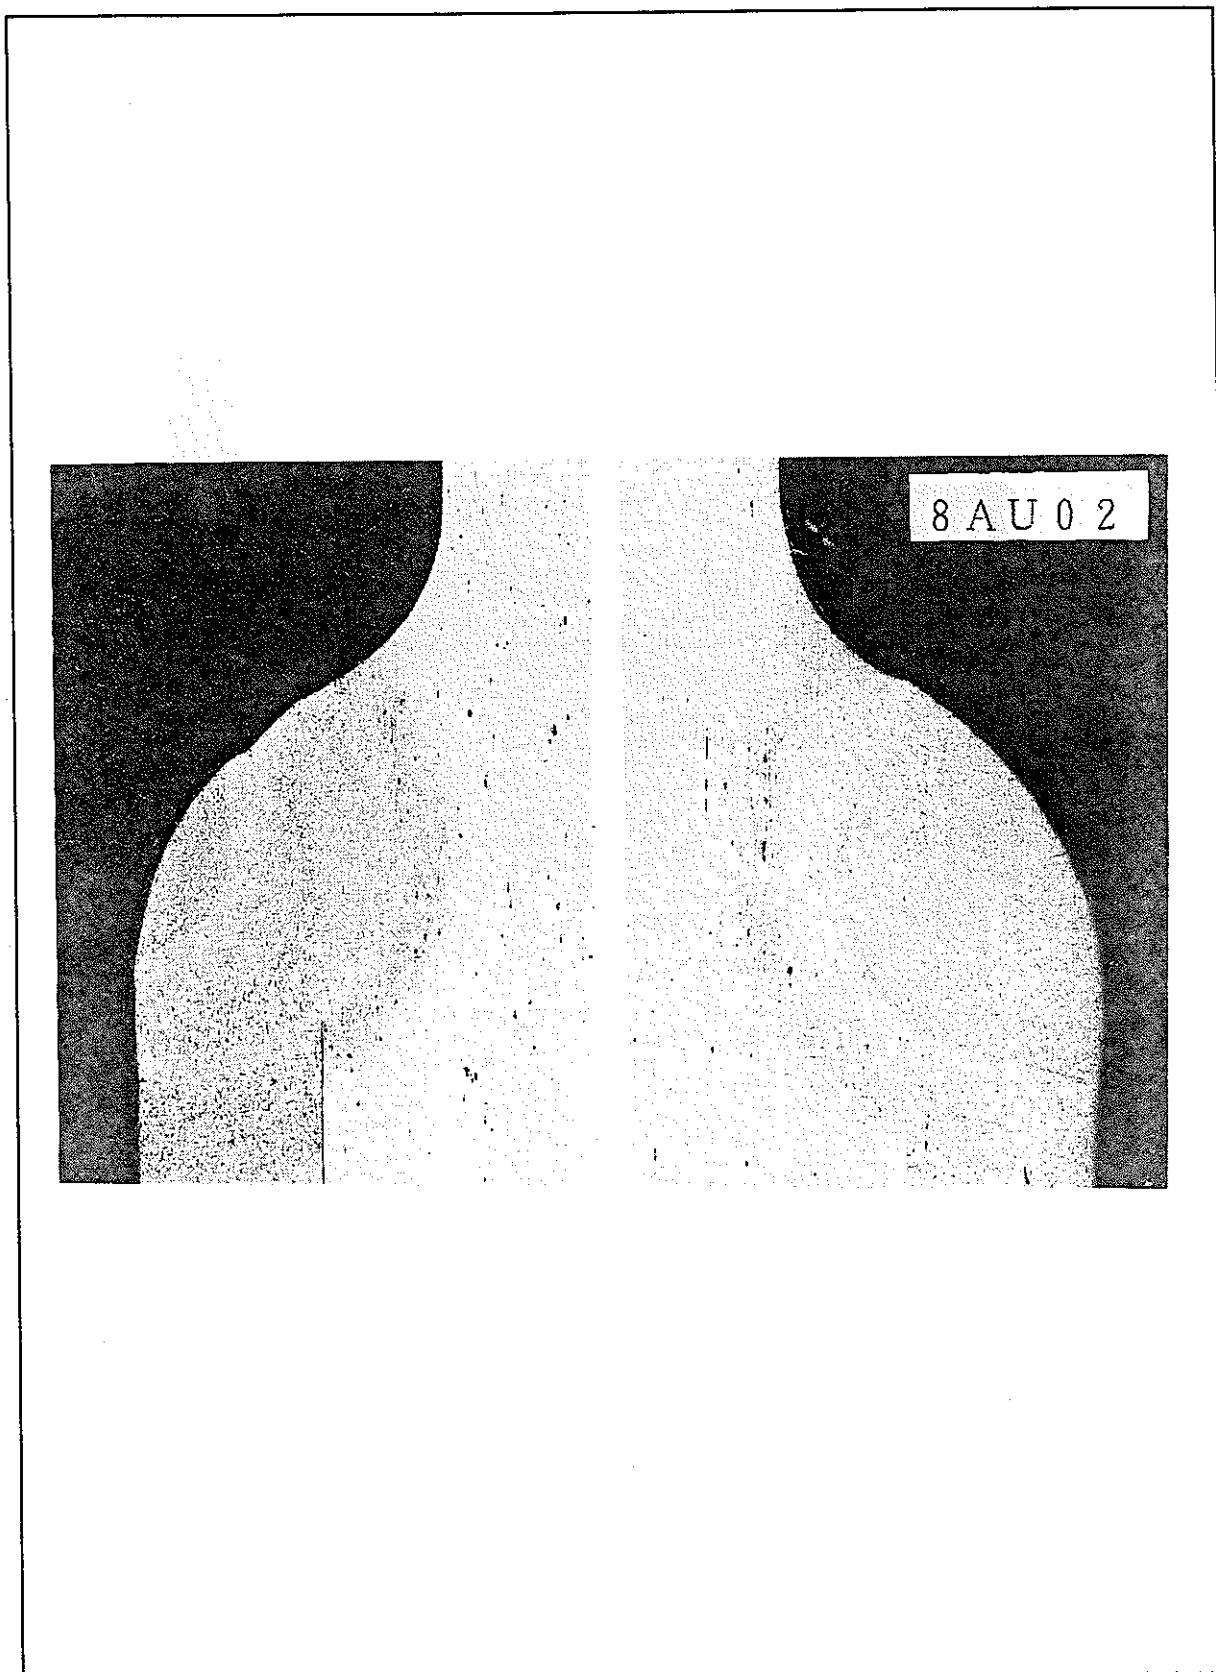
上部端栓溶接施行断面金相写真 (HT 9M)
